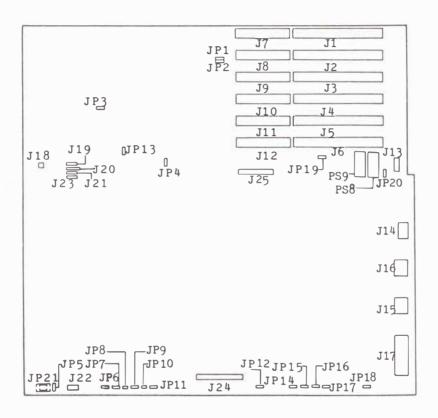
Jumper und Anschlüsse der Hauptplatine
